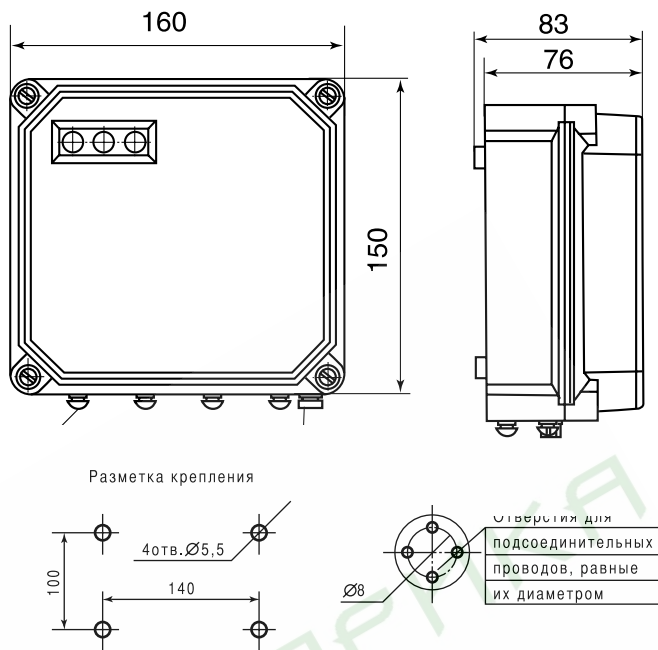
Габаритные, установочные размеры передающего преобразователя (ППР)
